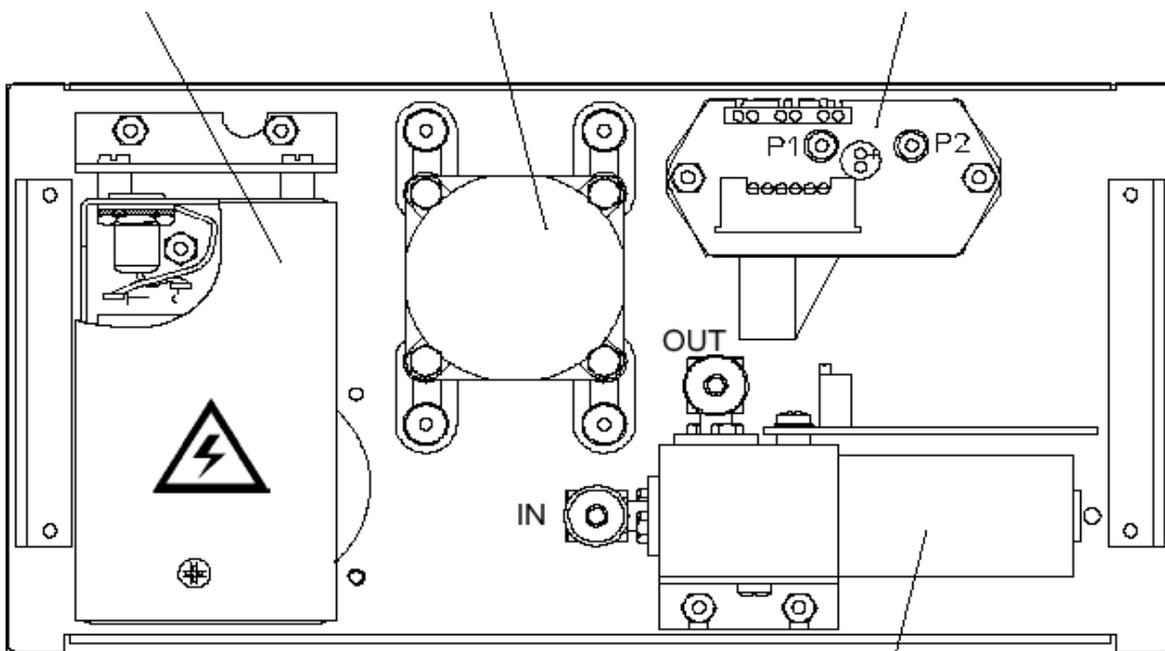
Módulo analizador MLT 1 (plataforma de montaje), panel frontal, vista frontal
